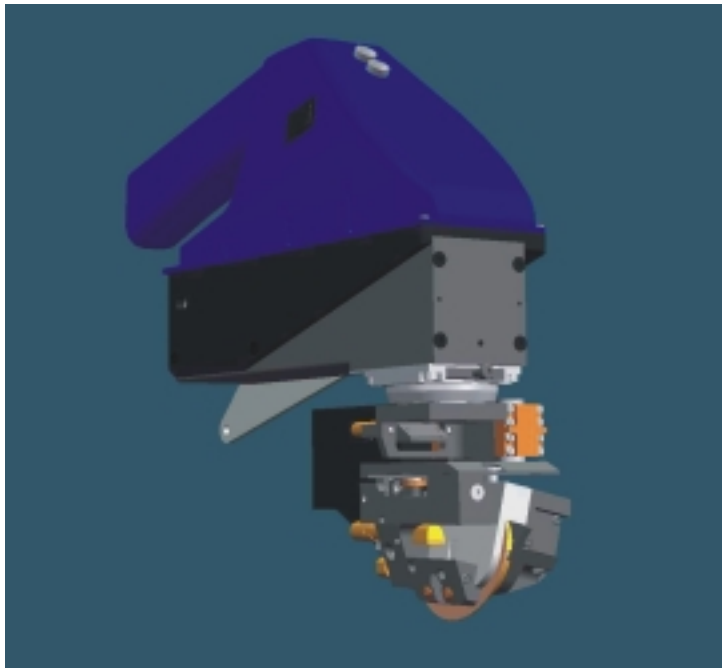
Konzept eines Werkzeuges zum Schweißen kurzer Heftnähte
